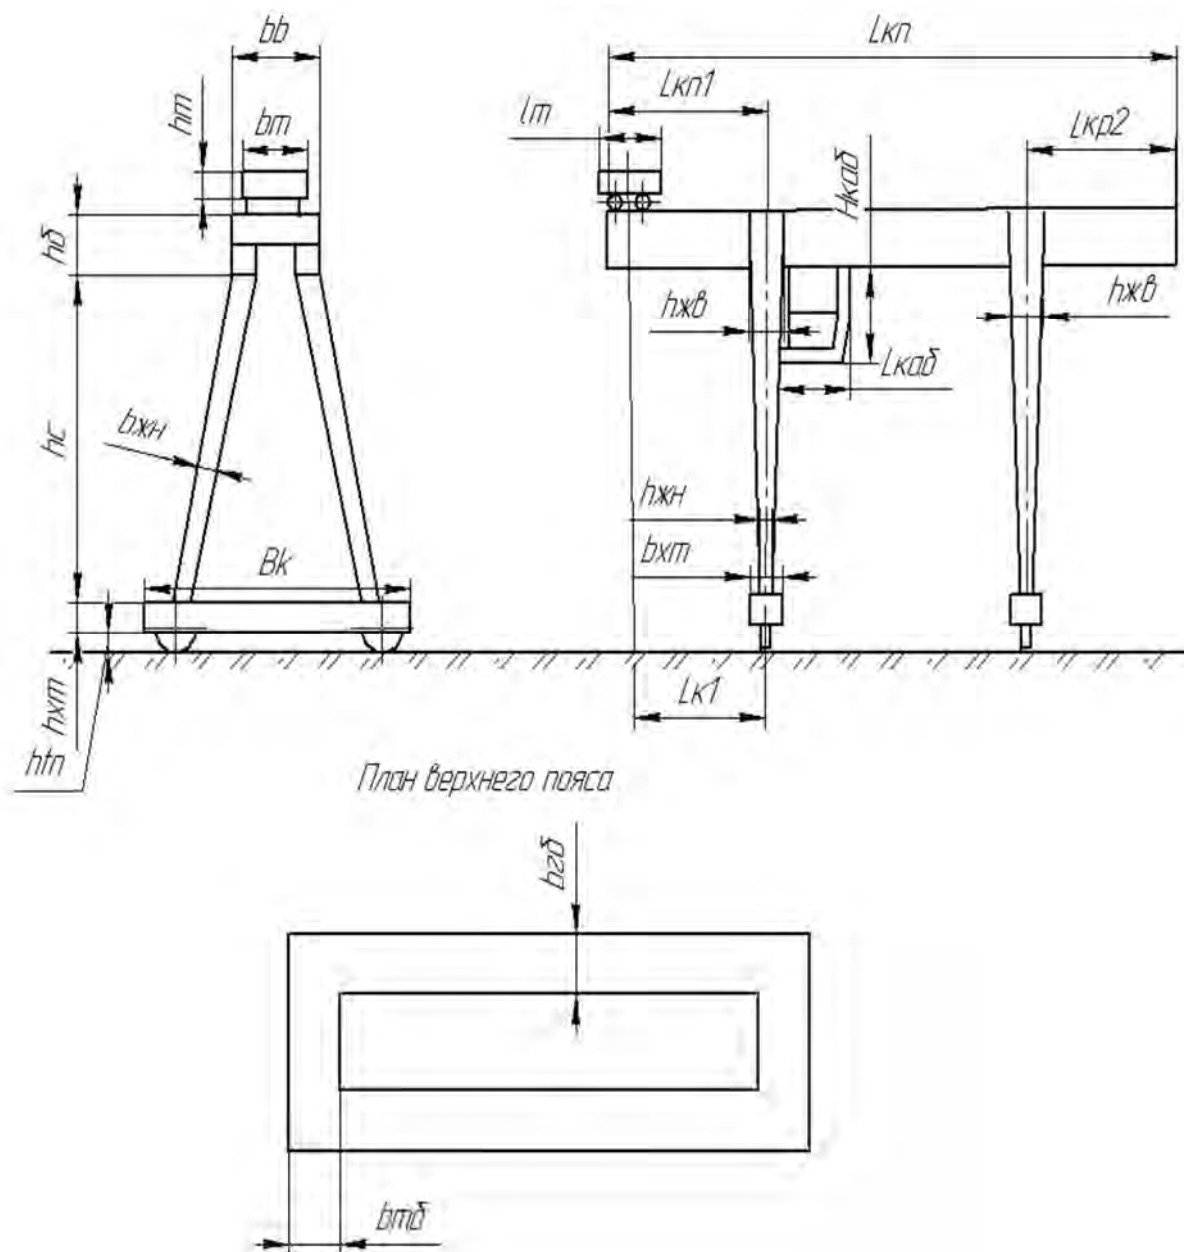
Расчетная схема для определения ветровых нагрузок
